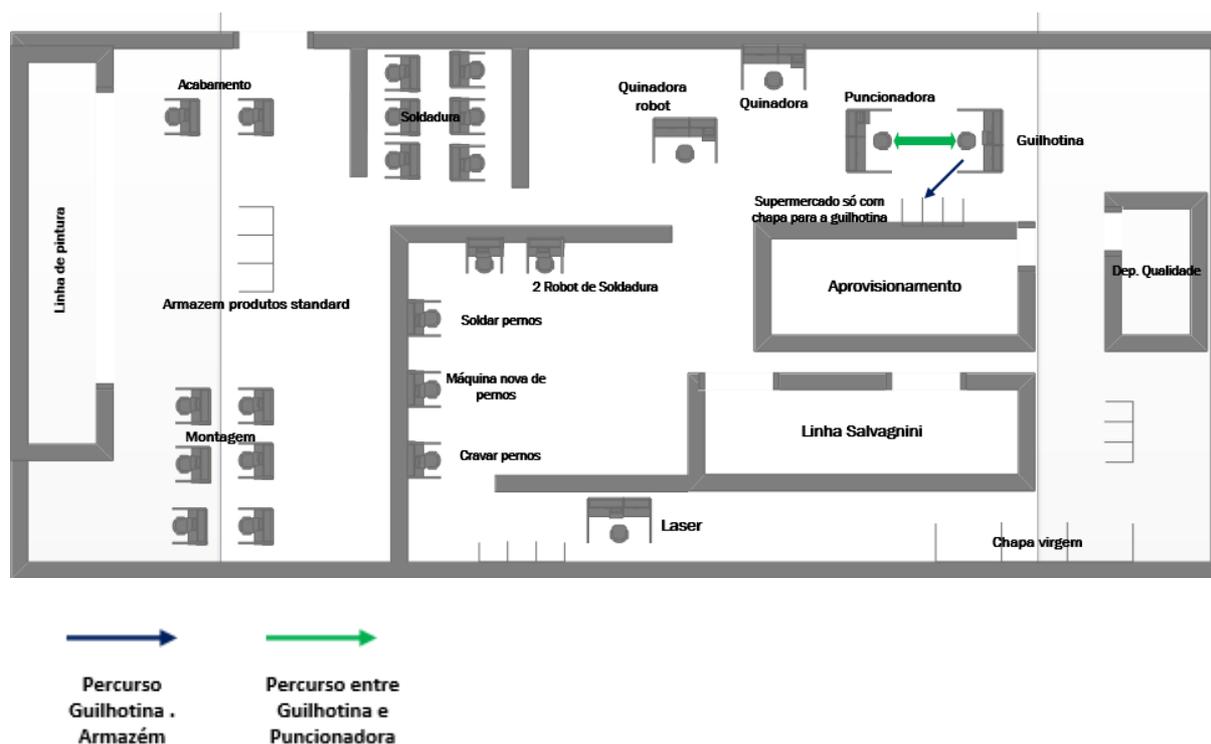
Layout da proposta de melhoria na secção da Guilhotina
